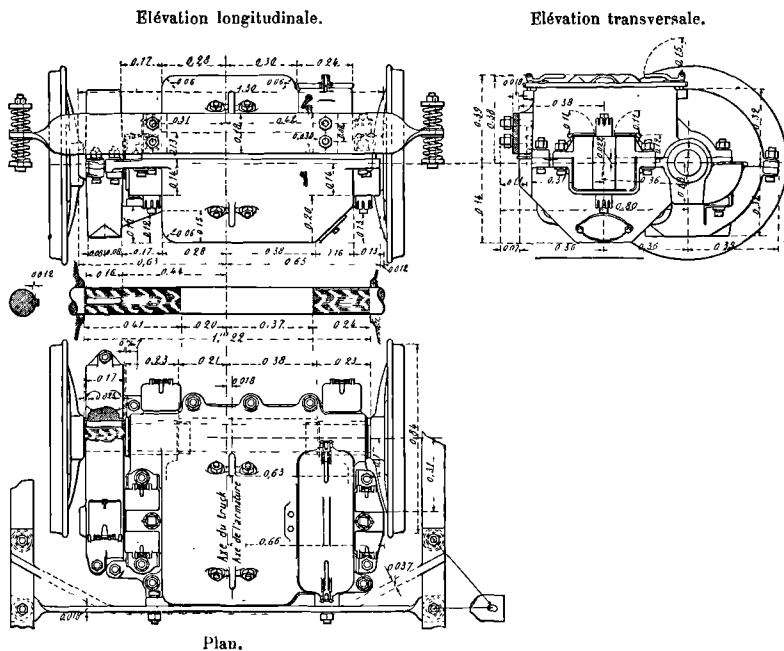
Dessins d'ensemble du moteur G. E. 51.
